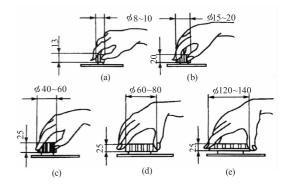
目镜尺寸 Fig. 5 Size of the eyepiece
